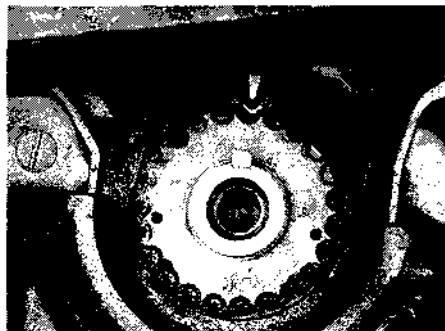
, б. Метки звездочки коленчатого вала (двигатель с одним распределительным валом)
